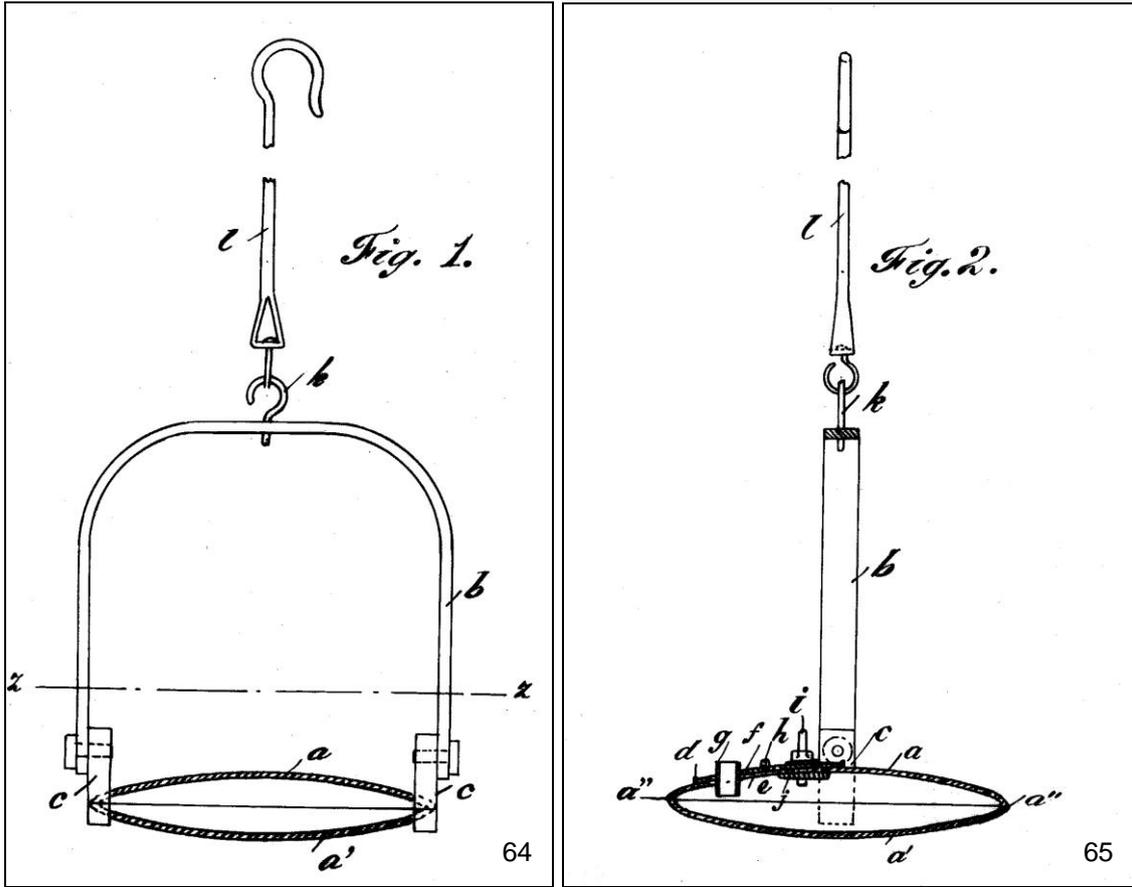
Detalle del perfil (Arch. J.M. Sanchis)
